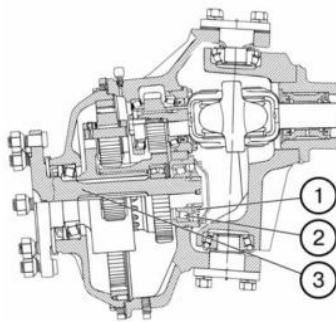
Проверка зазоров в подшипниках передних колес
